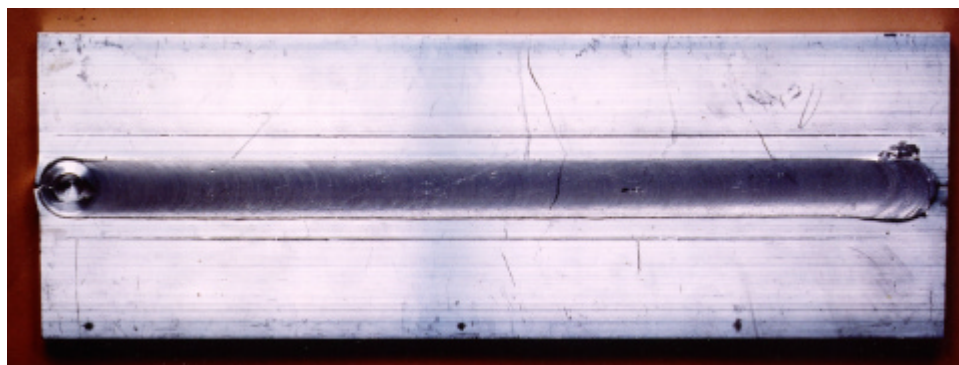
Prinsippet bak FSW [*Production of wide aluminium profiles by solid-state friction stir welding*]. Ole T. Midling og Helge G. Johansen.].
